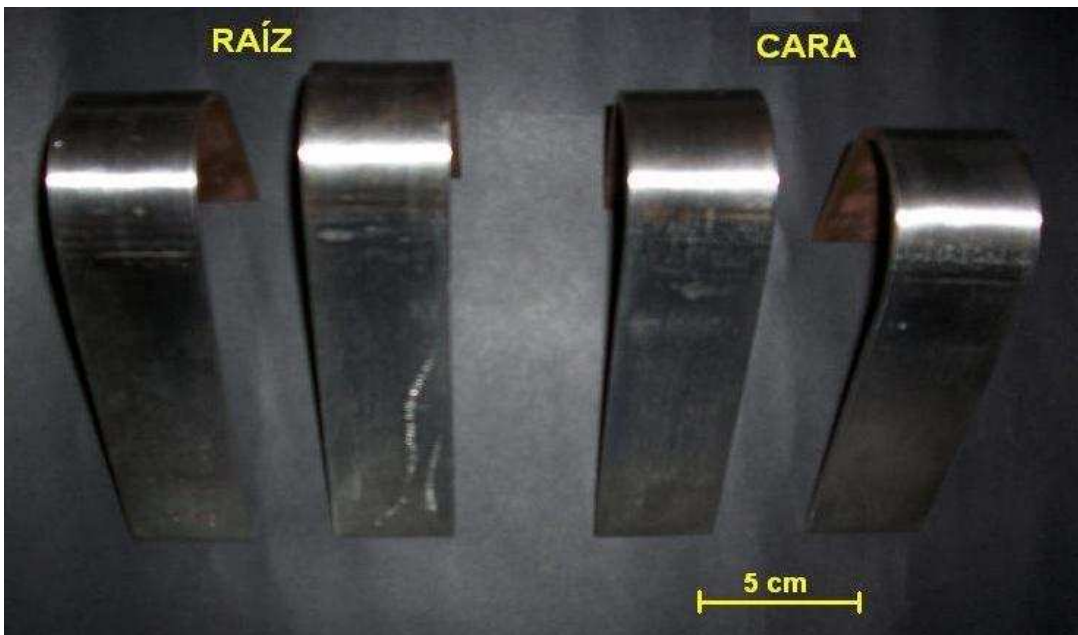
Ensayo de doblez de cuatro probetas de unión disímil de Acero Inoxidable Austenítico AISI/SAE 304 y ASTM A569, soldadas con un electrodo ER309L (vista superior).
